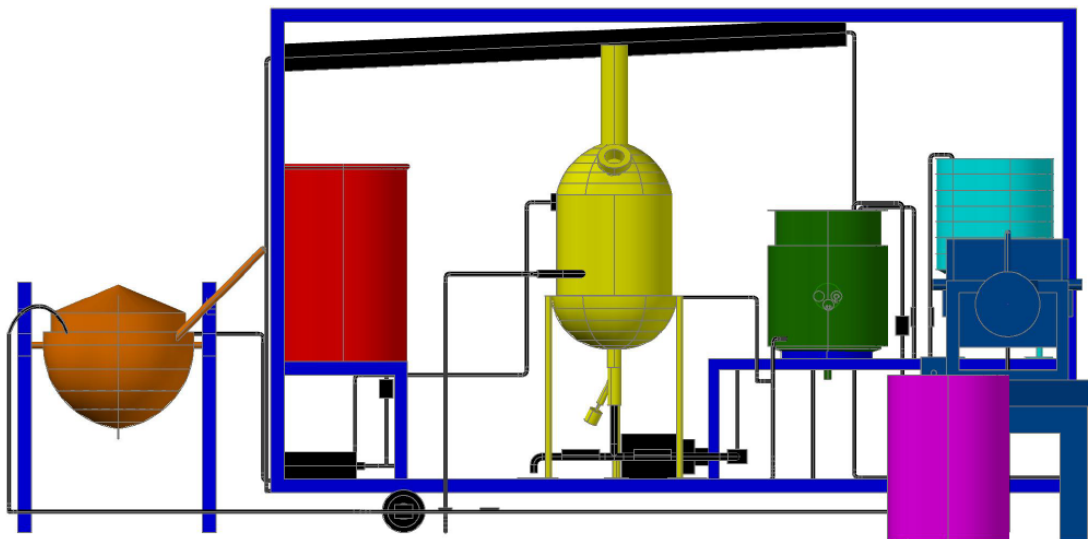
Vista lateral izquierda del modelo de la planta piloto
